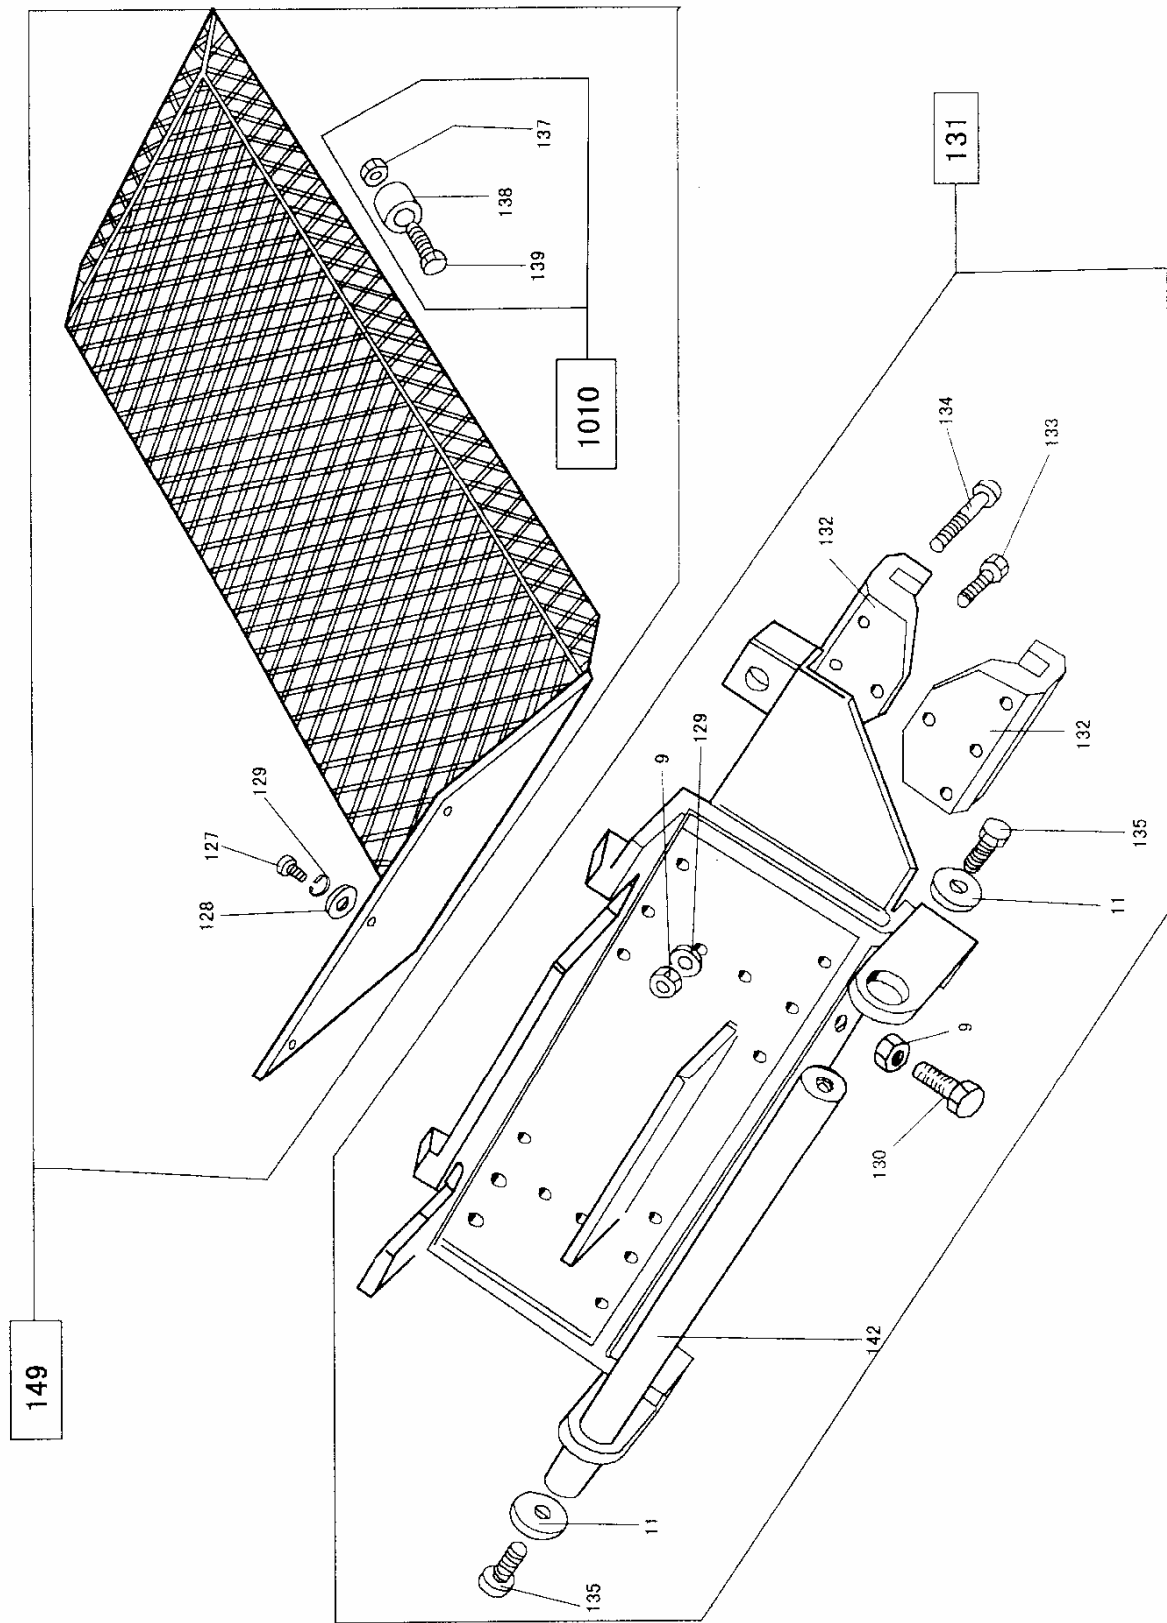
WERKZEUGAUFNAHMEARM-MOUNTING ARMBRAS DE MONTAGE
